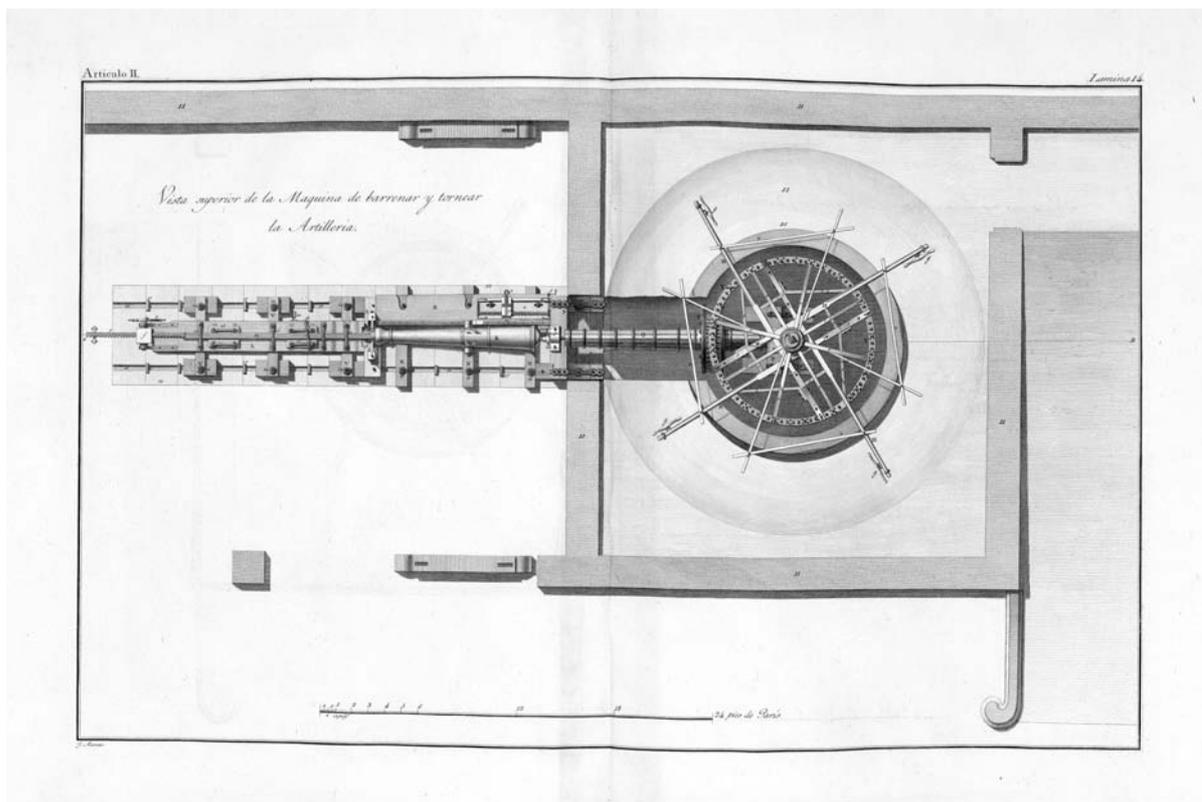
Plano de la máquina para barrenar y torneear las piezas de artillería que actualmente está en uso en nuestras fundiciones. Morla, 1803.
